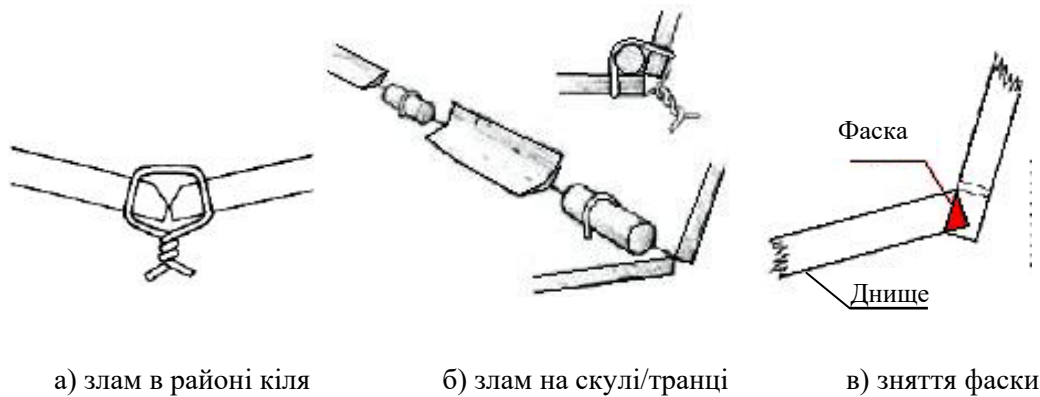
Підготовка до з'єднання кромки обшивки із фанери
